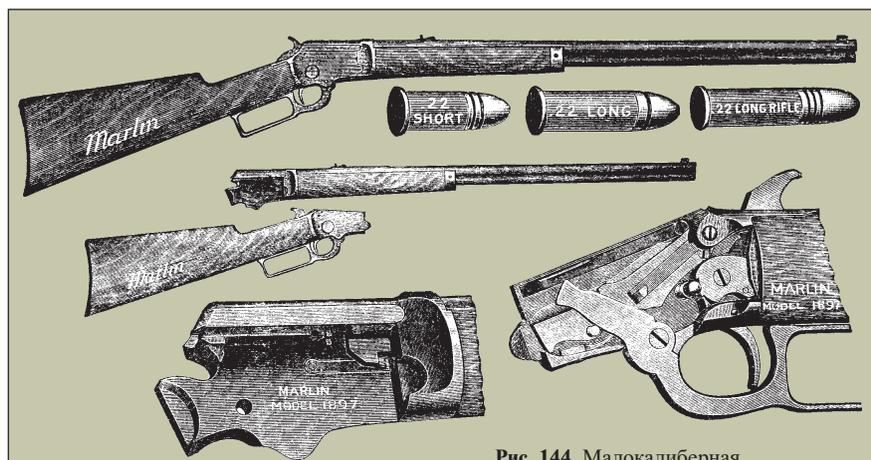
Малокалиберная винтовка Марлин образца 1897 г.
